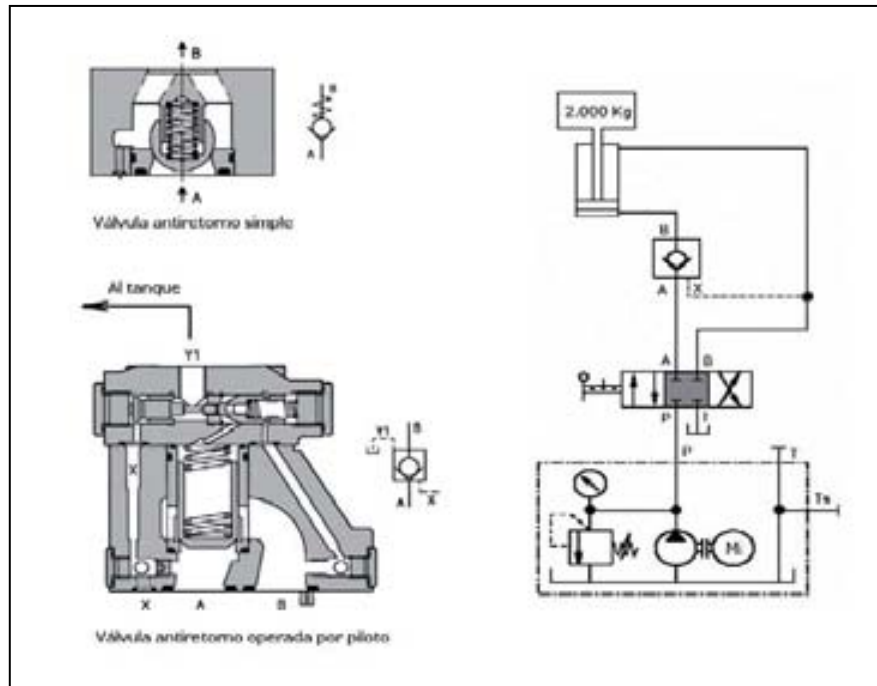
Válvula Antiretorno. Fuente: Denison Hydraulics
